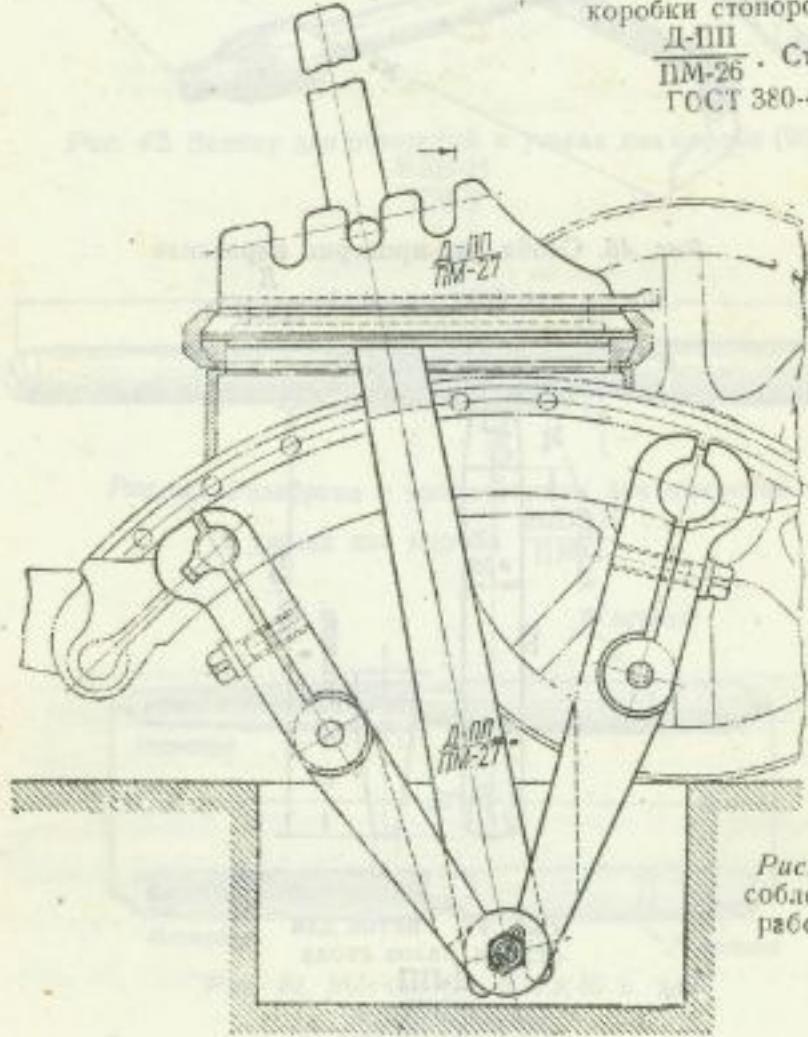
Приспособление для приработки стола на дугах Д-ПП ПМ-27.
